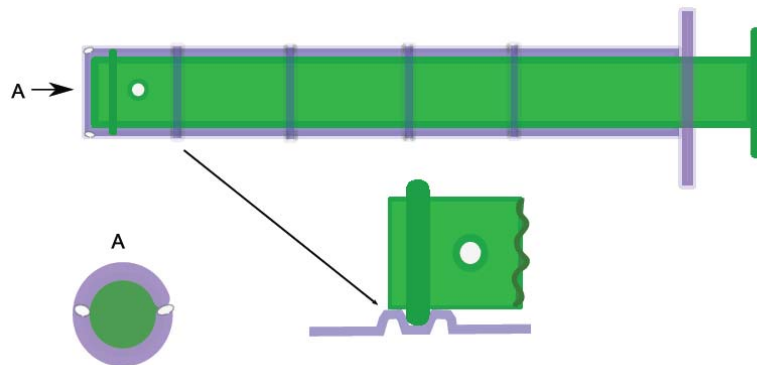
Modèle à piston droit (vue en coupe et section).
